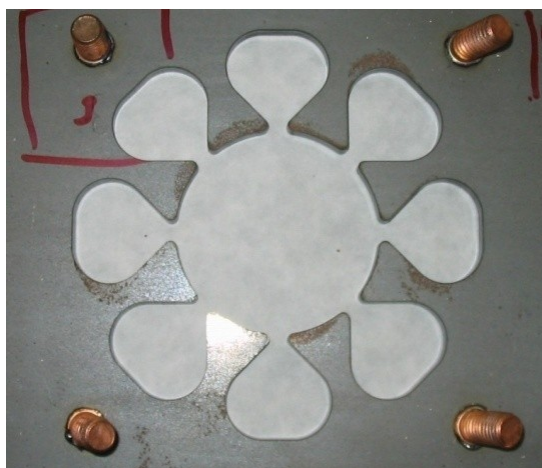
Detail polotovaru zkušební spoje č. 2.
